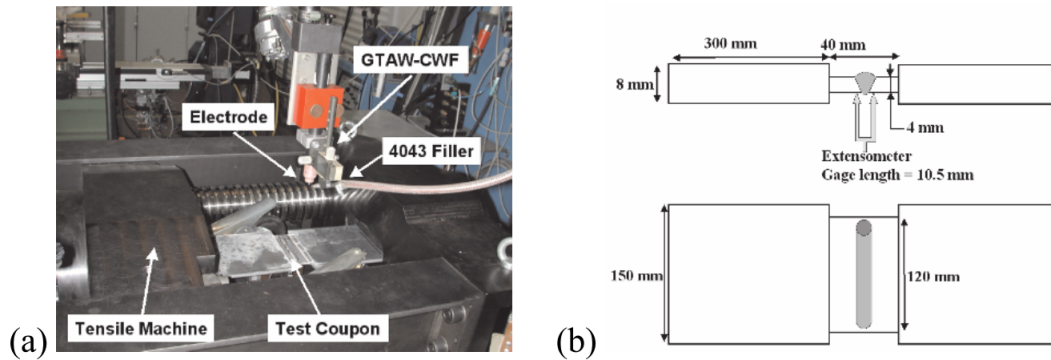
(a) Vue d'ensemble de la machine d'essai CTW ; (b) éprouvette utilisée [CC08]
